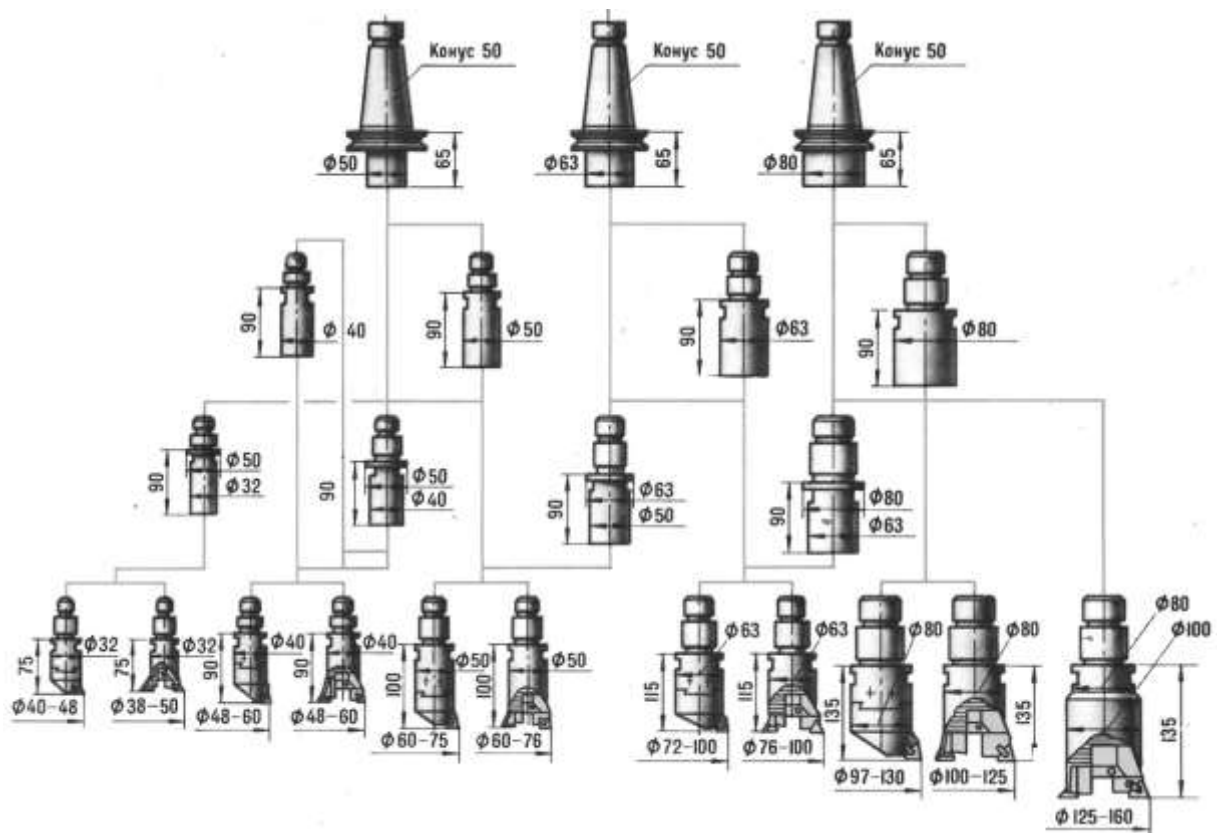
Уніфікована система модульного інструмента для свердлильно-фрезерно-розточний обробки
